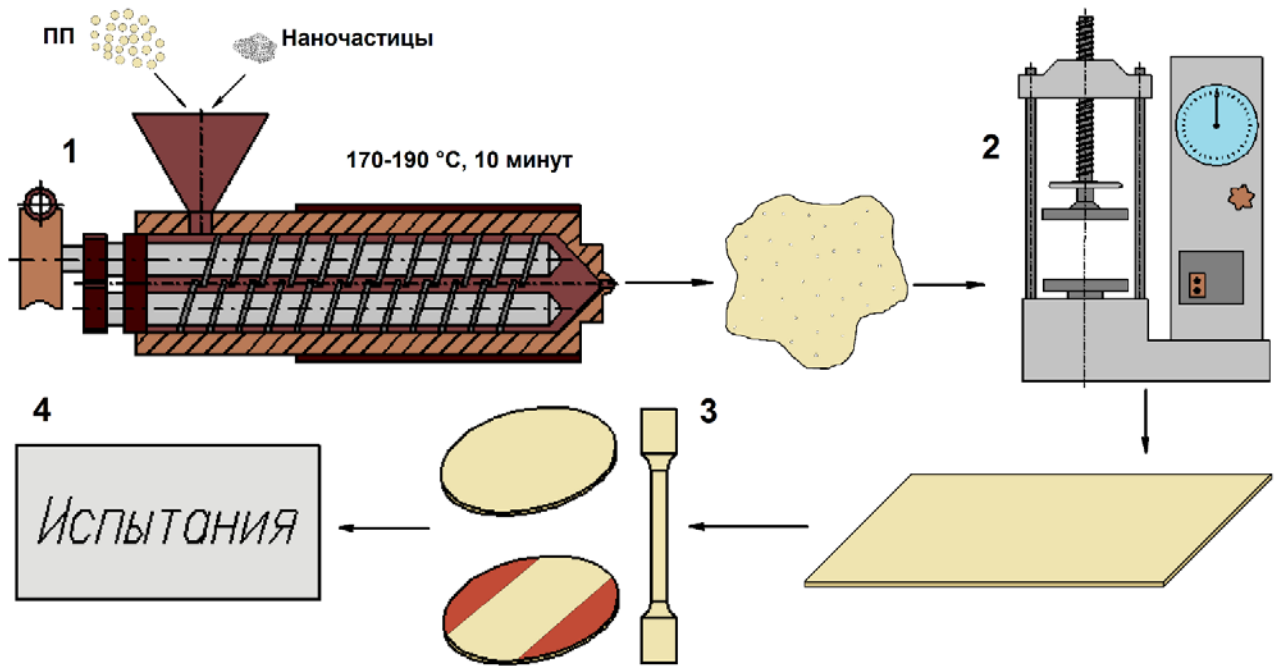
Схема получения образцов нанокомпозитов: 1-смешивание полимера и наночастиц на двухшнековом экструдере, 2-выдержка полимера под давлением в форме, 3-изготовление образцов для испытаний, 4-проведение испытаний
